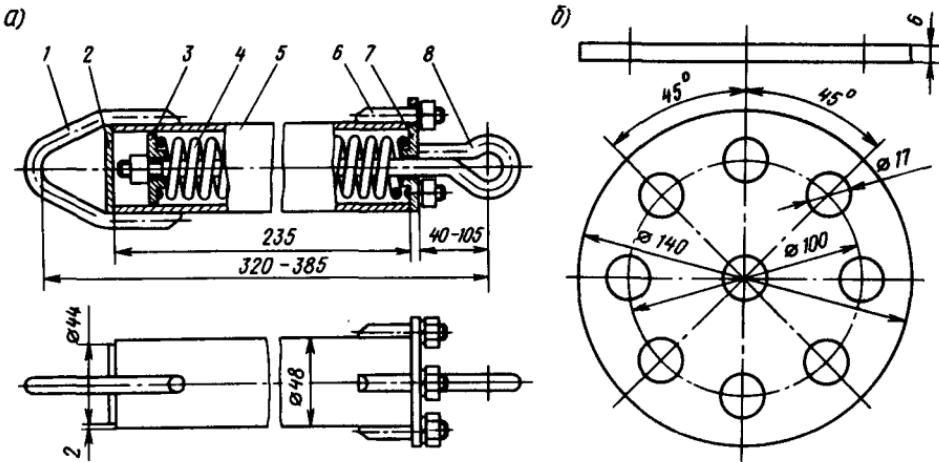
Пружинный компенсатор (а) и воздушное кольцо (б):
